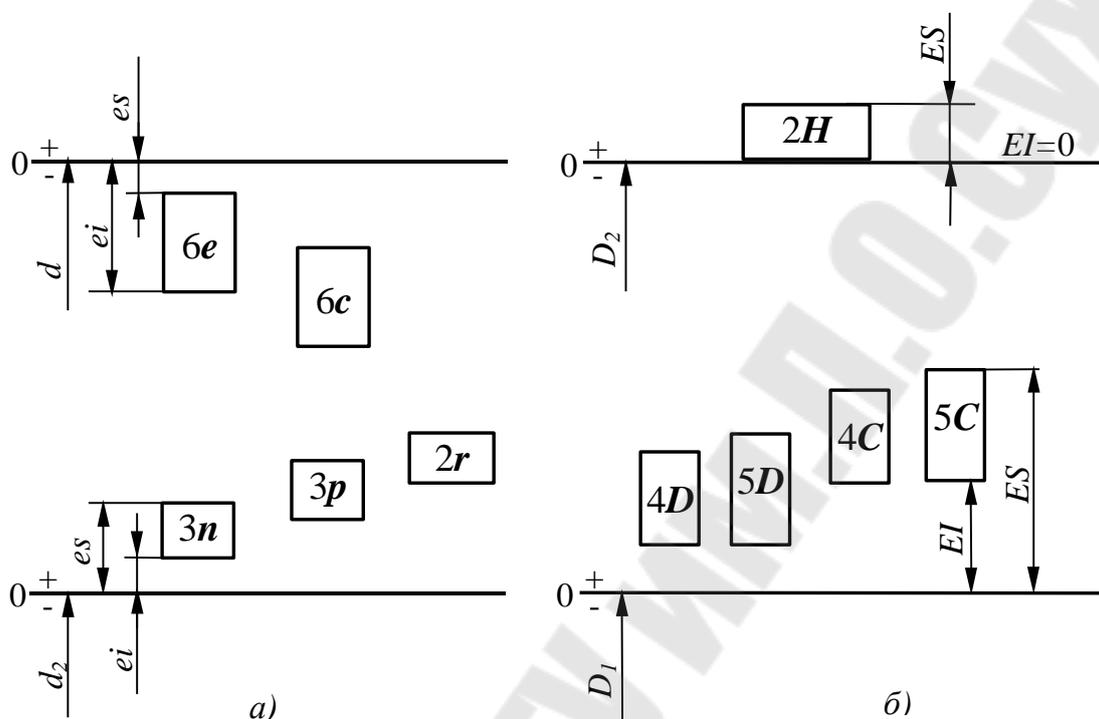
Расположение полей допусков метрической резьбы с натягом: а – для наружной; б – для внутренней.
